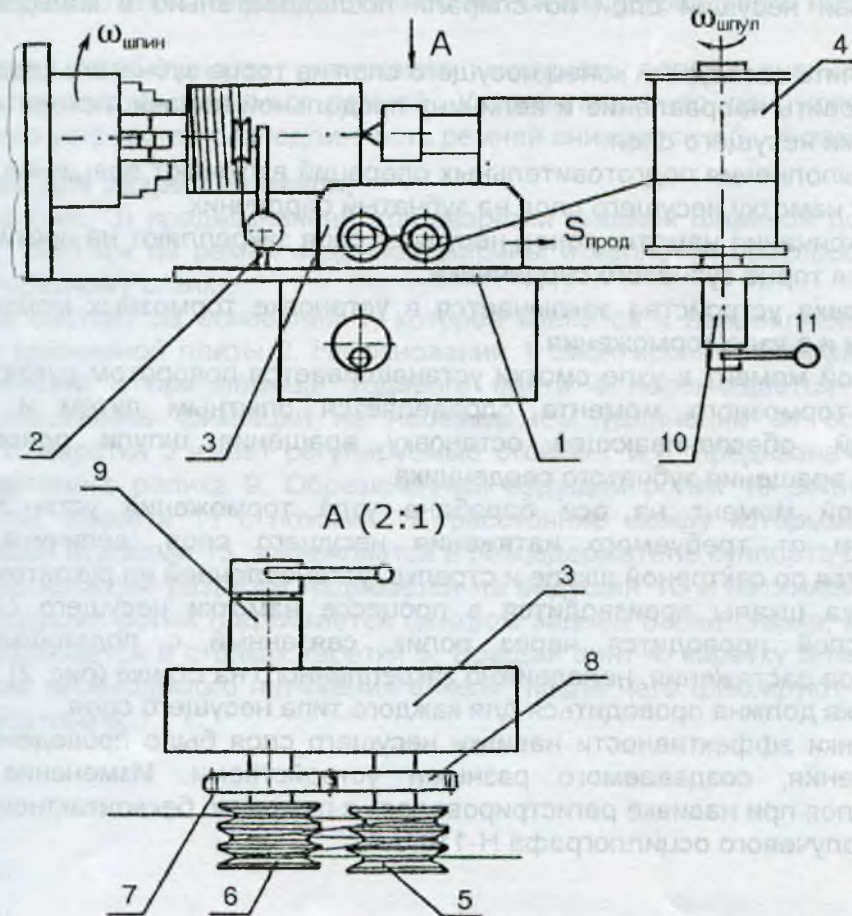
Устройство для навивки несущего слоя: 1 – основание; 2 – стойка; 3 – узел торможения; 4 – узел смотки; 5, 6 – барабаны; 7, 8 – зубчатые колеса; 9 – регулируемый тормоз узла торможения; 10 – ось для установки шпули с несущим слоем; 11 – регулируемый тормоз узла смотки
